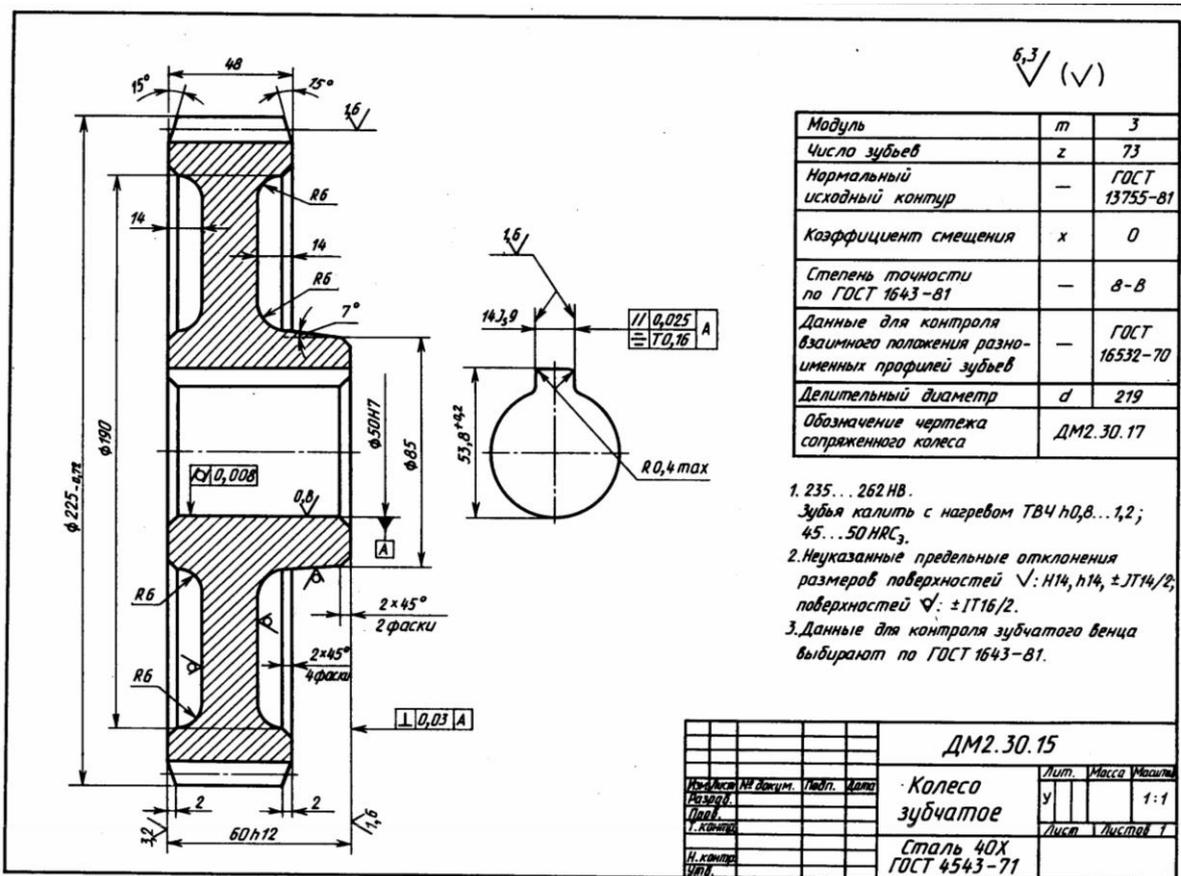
Чертеж детали «Колесо зубчатое»
